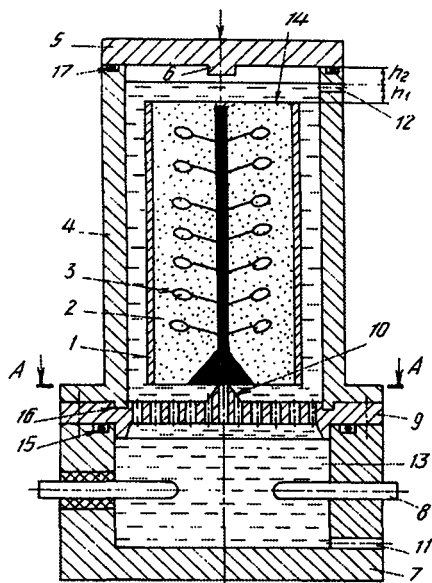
Схема установки для очистки отливок ювелирных изделий
